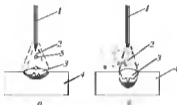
Струйный (а) и крупнокапельный (б) перенос электродного металла: 1 — электрод, 2 — дуга, 3 — сварочная ванна, 4 — изделие, 5 — капли электродного металла
